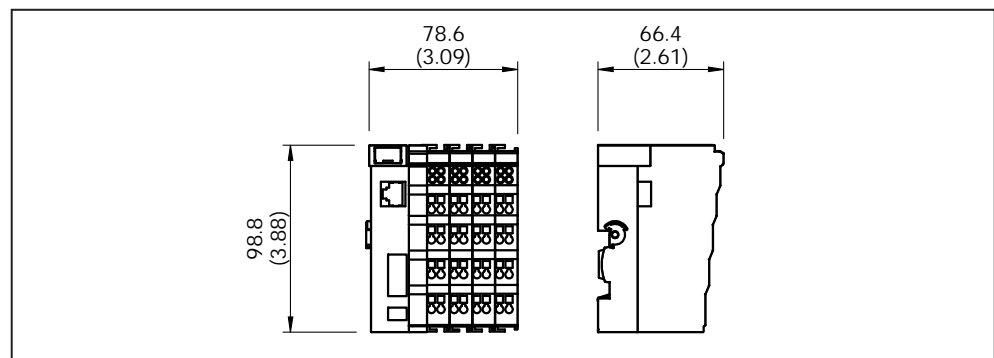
Размерный чертеж аналогового модуля ВAM100
